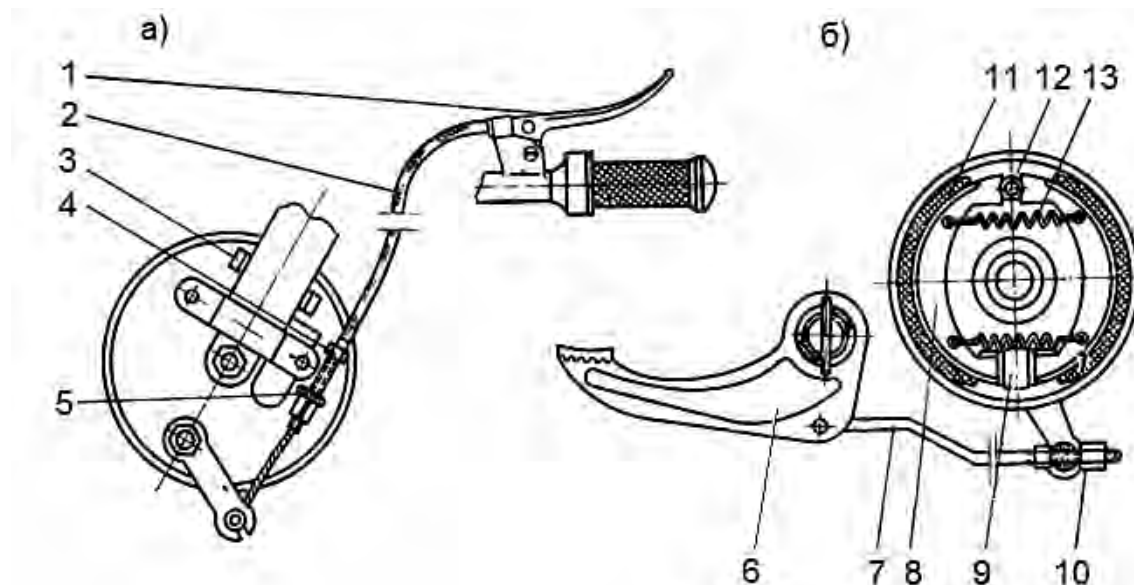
Барабанный тормоз двухколесного транспортного средства с разжимным кулаком: а – передний тормоз; б – задний тормоз; 1 – рычаг тормоза; 2 – трос; 3 – реактивный упор; 4 – регулировочный винт; 5 – контргайка; 6 – тормозная педаль; 7 – тяга; 8 – тормозная колодка; 9 – кулачок тормоза; 10 – регулировочная гайка; 11 – накладка; 12 – ось колодок; 13 – пружина колодок
